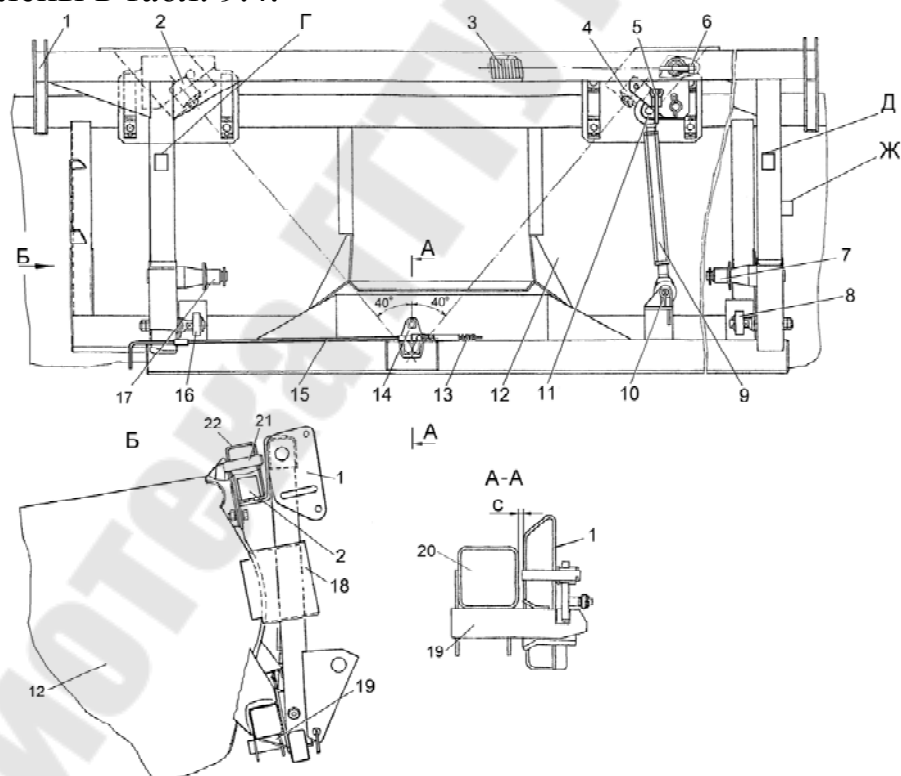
Схема навески рамки переходной на жатку: 1 – рама; 2, 4, 7, 8, 16, 17 – ролики; 5, 10, 21 – пальцы; 3 – пружина сдвоенная; 6 – болт регулировочный; 9, 15 – тяги; 11 – рычаг поперечного копирования; 12 – жатка\*; 13 – пружина; 14 – фиксатор; 18 – кронштейн крепления гидромотора; 19 – палец опорный; 20 – труба жатки; 22 – ловители жатки верхние; \* – жатка для трав или жатка для зерносенажных культур; Г, Д, Ж – места установки пальцев
